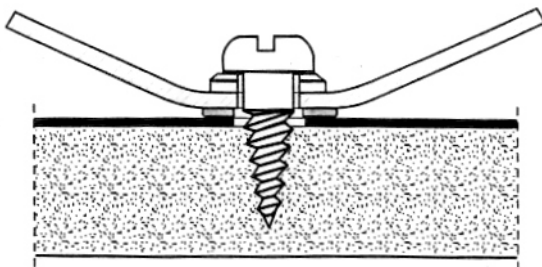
Schraubverbindung. Der Schichtstoff wurde vor der Verschraubung mittels einer etwa 2 bis 4 mm größeren Bohrung (als der Schraubendurchmesser) entfernt.
